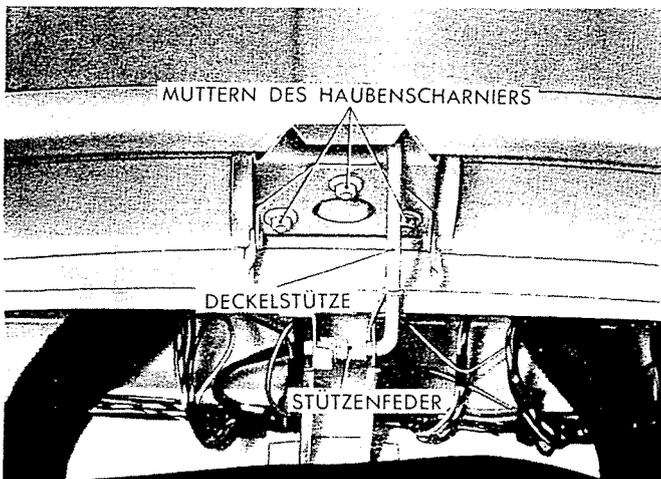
Ansicht des geöffneten Haubendeckels mit Scharnier und Stütze.
